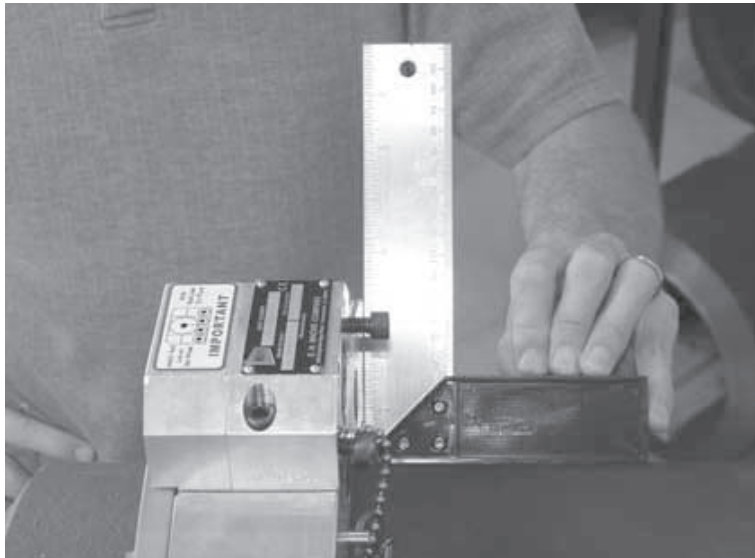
Use la escuadra para asegurarse de que la máquina esté perpendicular al tubo.
